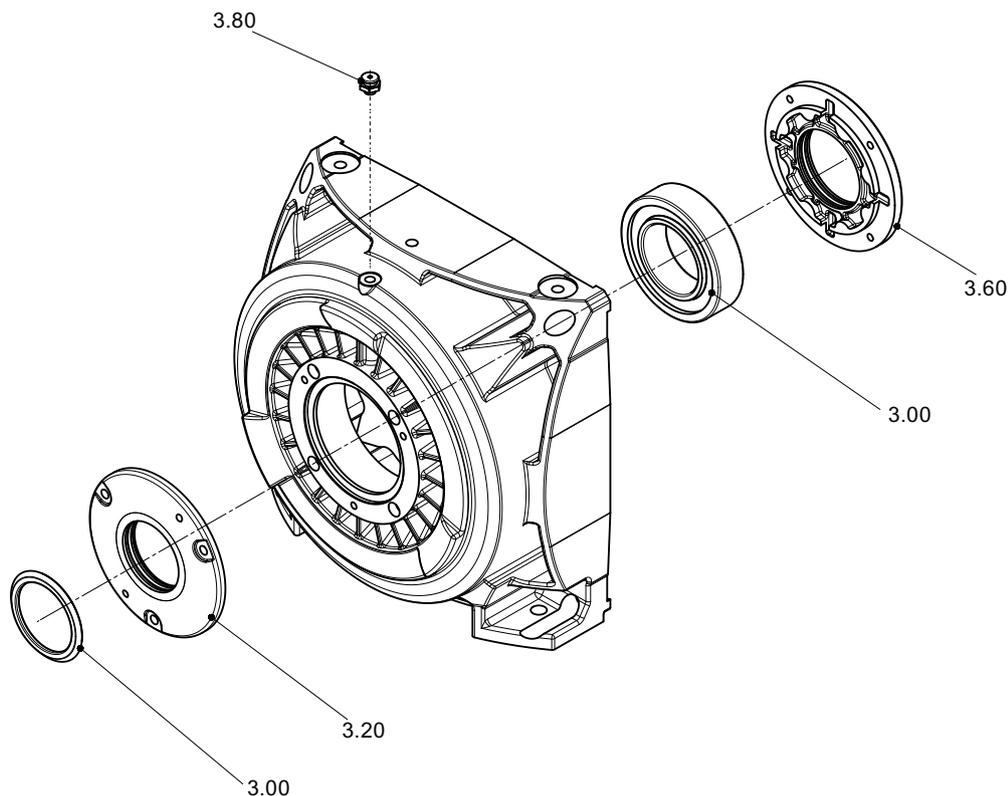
Узел подшипника качения приводная сторона, ременной привод, с дополнительной смазкой
